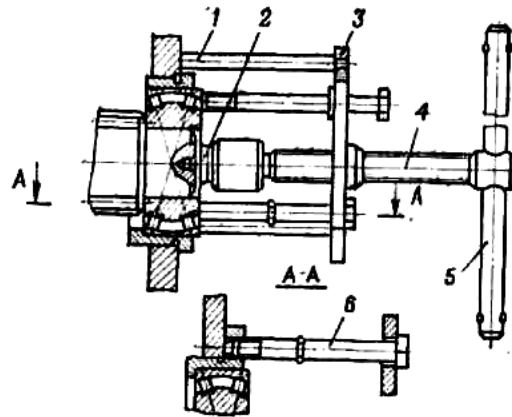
Пристосування для зняття заднього підшипника проміжного вала I-801.31.000: 1 - упор, 2 - наконечник; 3 - плита; 4 - гвинт, 5 - рукоятка; 6 - болт
